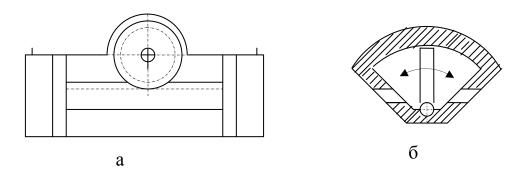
Поворотные пневмогидродвигатели: а - поршневой; б – шиберный.
